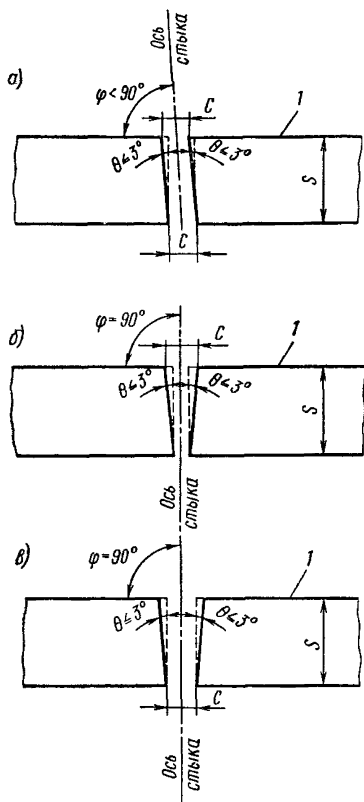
Схема сборки стыковых соединений с перпендикулярно обработанными кромками:
